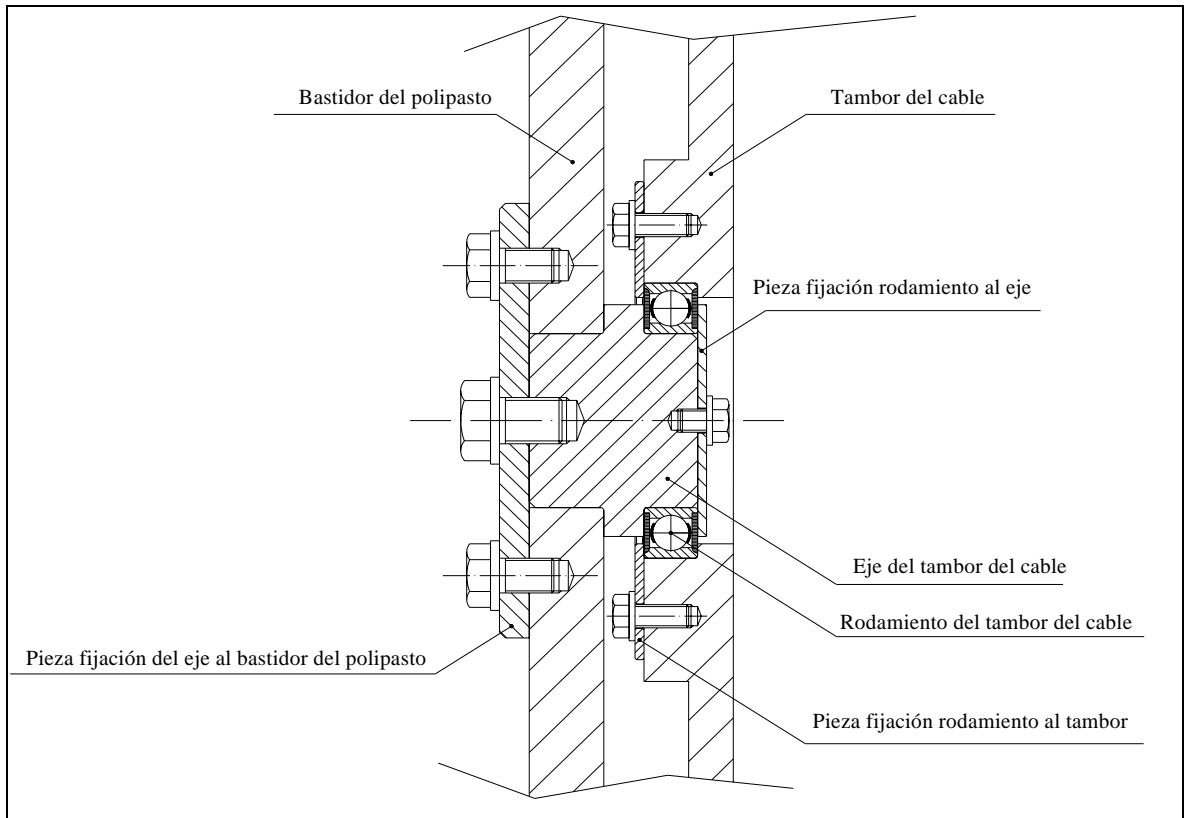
Detalle montaje del eje del tambor del cable.
